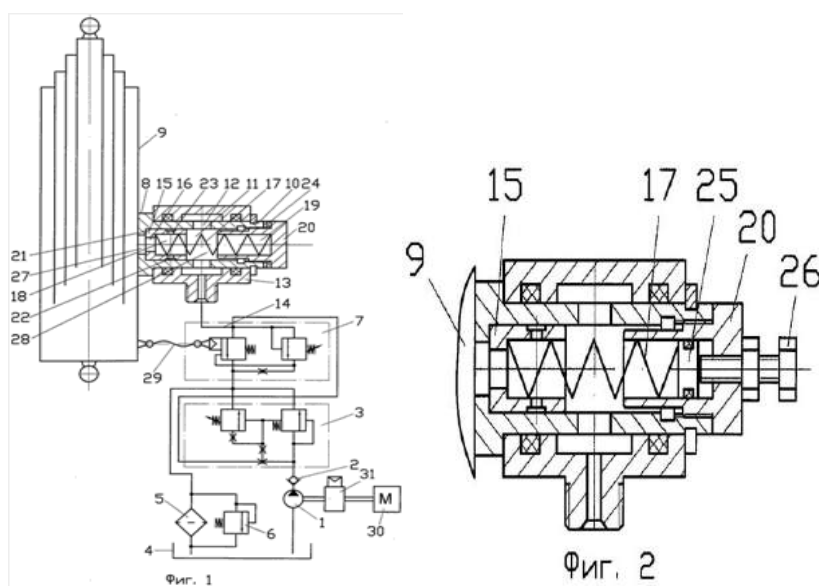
Конструктивная схема устройства для подъема платформы автомобиля-самосвала и регулировочный клапан с регулировкой усилия пружины плунжера регулировочным болтом
